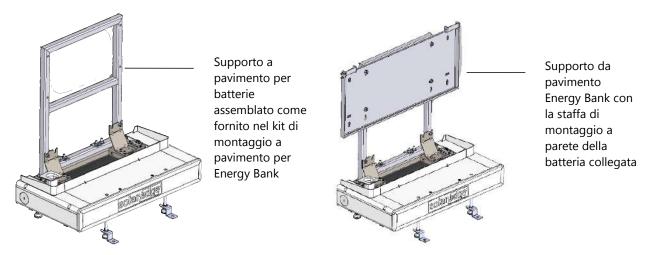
Supporto da pavimento assemblato e supporto da pavimento con staffa di montaggio a parete della batteria
